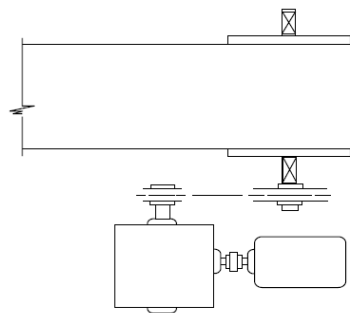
Motor, reductor de ejes perpendiculares y acoplamiento directo al tambor.
